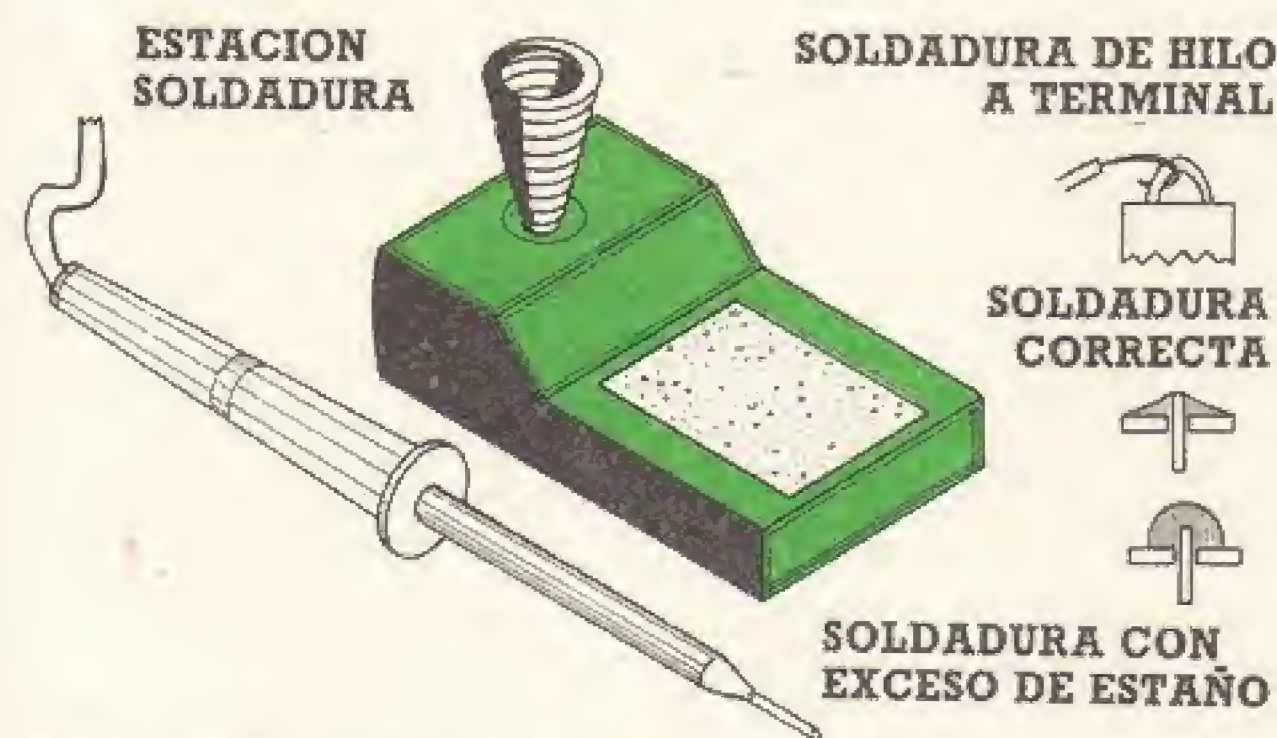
Estación de soldadura, soldaduras de terminal y de hilo.
